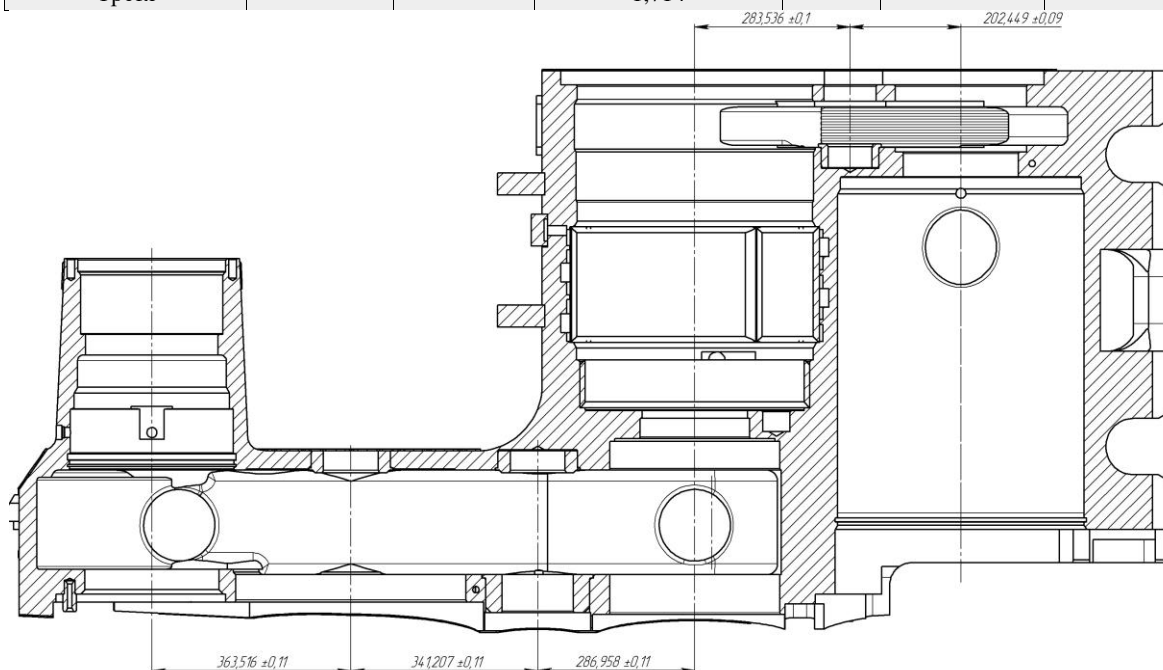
Ескіз корпусу редуктора різання очисного комбайна УКД200-500
